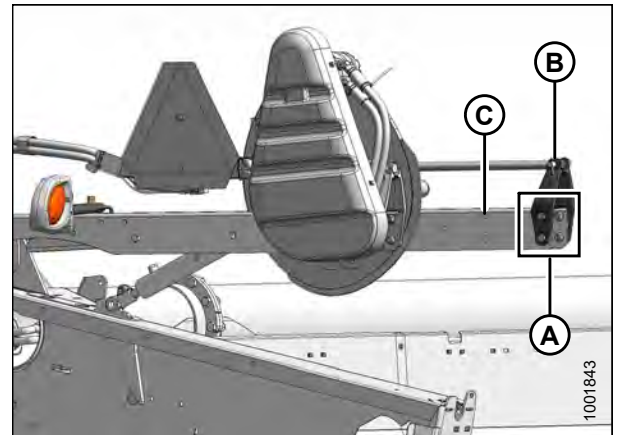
Rechter Haspel-Horizontalzylinder in Stellung „Vorne“
